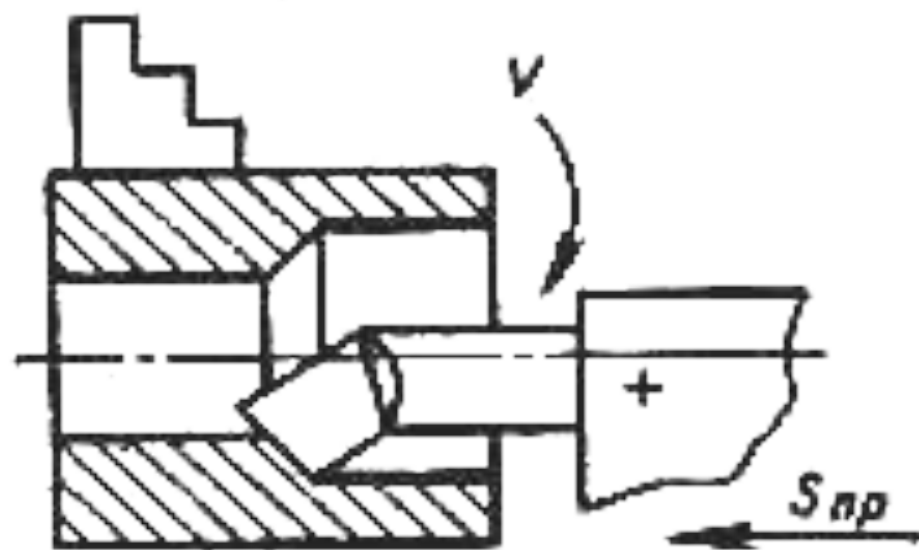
Расточный резец, применяемый на токарно-револьверных станках:
